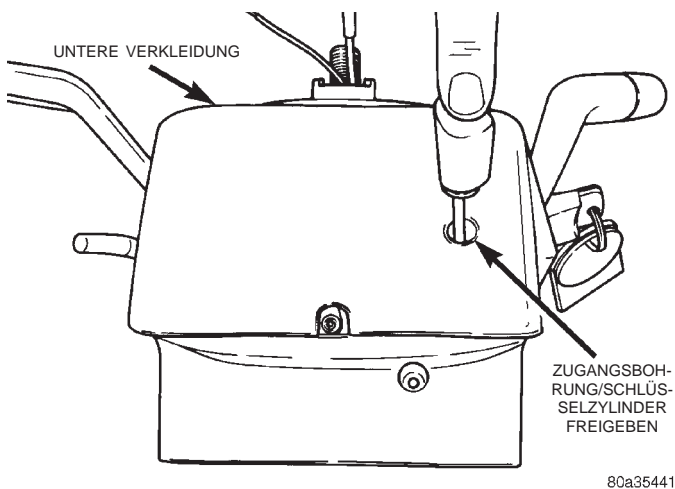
Zugangsbohrung/Schlüsselschlosszylinder freigeben
